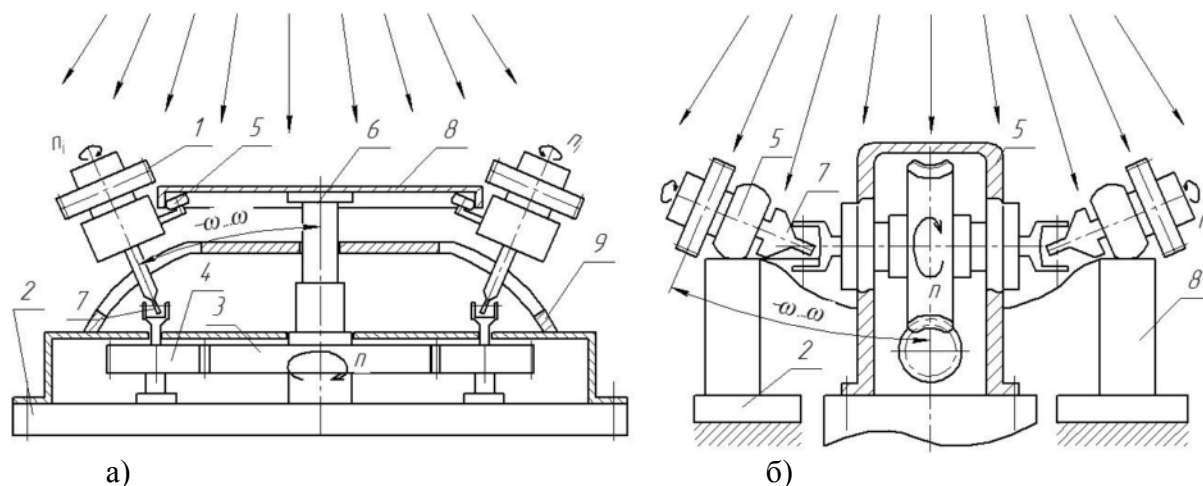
Устройства для ориентации и вращения заготовок зубчатых колес в процессе нанесения покрытий
